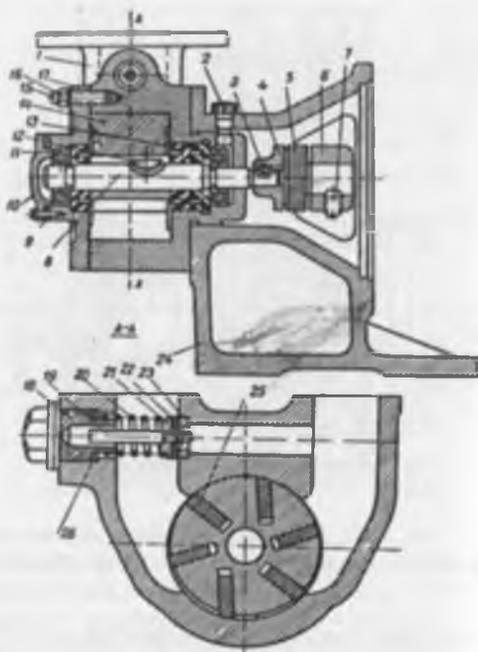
Бензонасос пластинчатого типа: 1 – корпус; 2 – маслѐнка; 3 и 12 – шпонки сегментные; 4 и 6 – полумуфты; 5 – звездочка; 7 – винт стопорный; 8 – вал; 9 – прокладка; 10 – крышка; 11 – подшипник шариковый; 13 – манжет уплотнительная; 14 – ротор; 15 – шпилька; 16 – гайка; 17 – крышка; 18 – пробка; 19 – шток; 20 – пружина клапана; 21 – шайба специальная; 22 – тарелка клапана; 23 – сегмент; 24 – стойка; 25 – лопатки; 26 – шайбы регулировочной пружины
